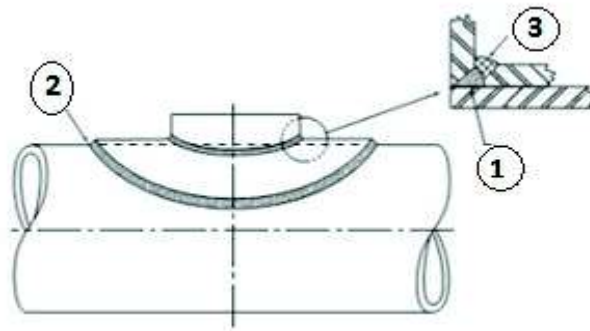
Detalle de la Junta soldada con la secuencia de soldadura recomendada.
